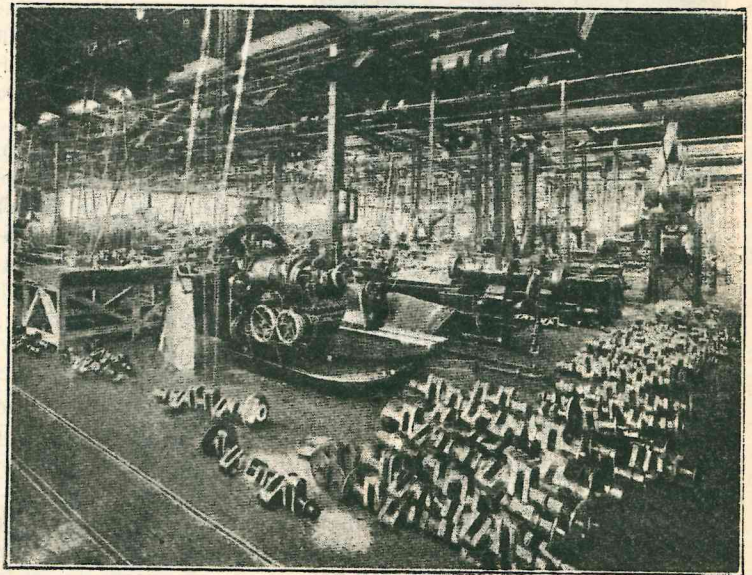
Внутренний вид механической мастерской авиа-моторного завода Ролльс-Ройс в Англии со стороны группы станков, занятых обработкой коленчатых валов.
